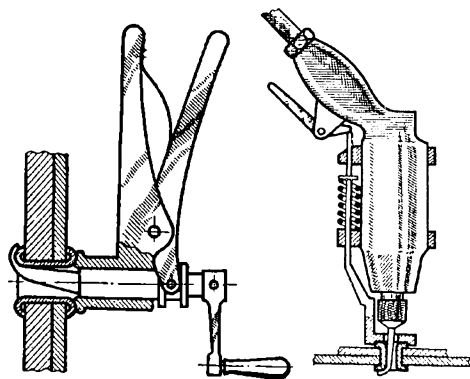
Развальцовка бурта трубчатой заклепки
